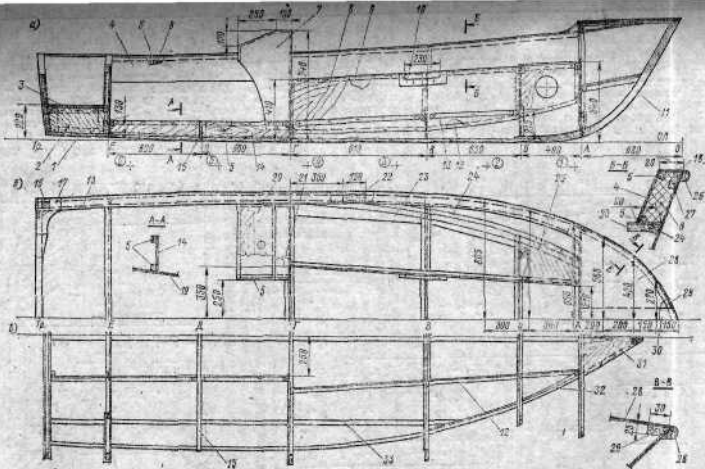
Конструктивный продольный разрез корпуса (а), вид сверху на набор (б) и на набор днища (в).
